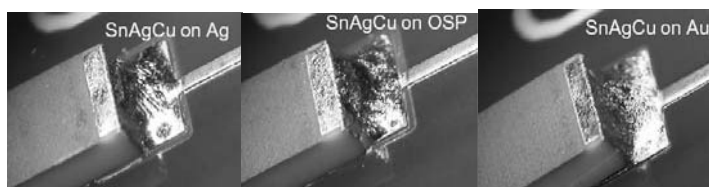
不同 PCB 表面保护层的无铅再流焊焊点
